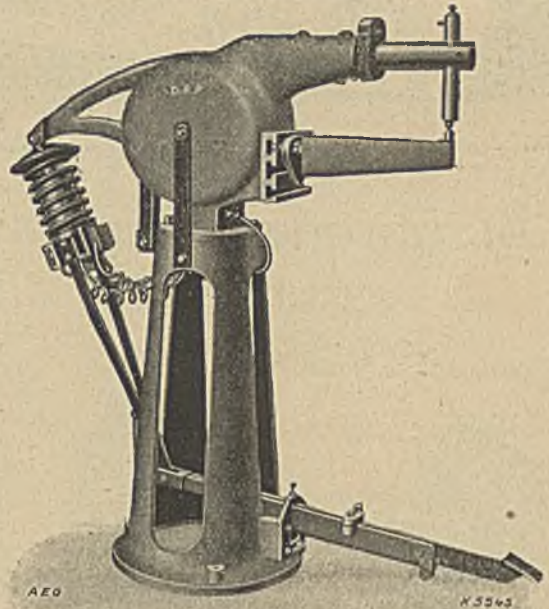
Punktschweißmaschine Type Pu.
